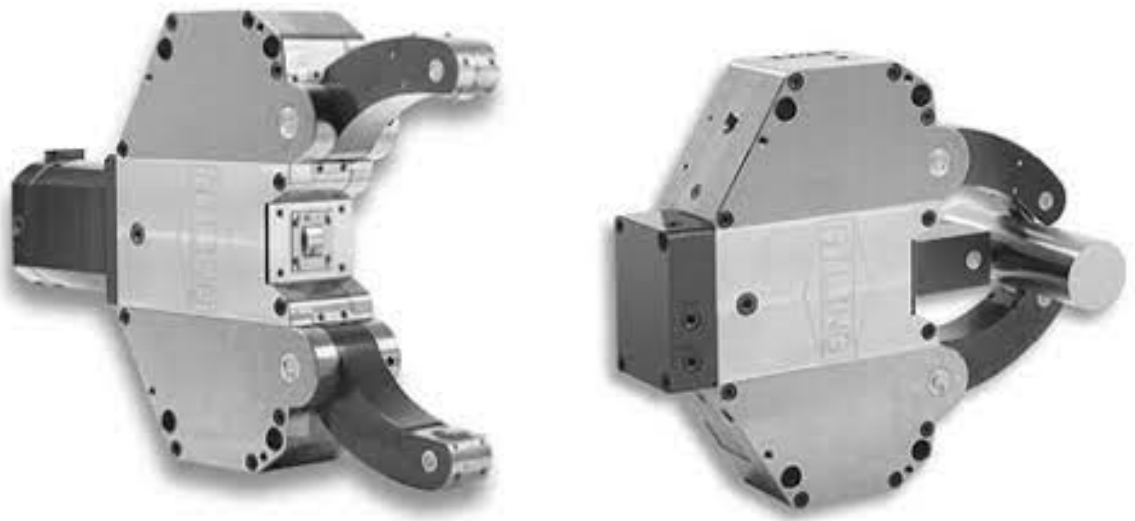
Люнет токарного верстата з ЧПУ
